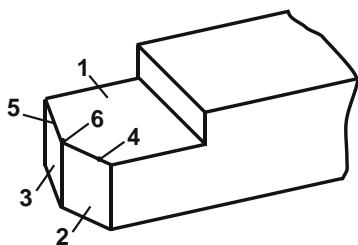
Загальний вигляд ріжучої частини різця
